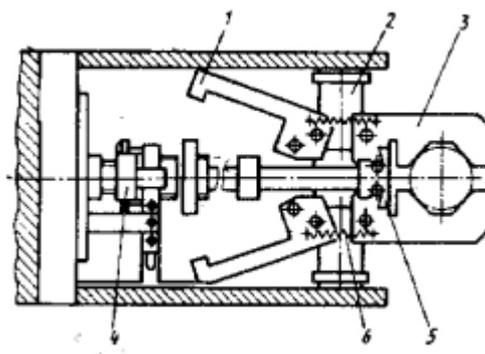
Захватное устройство с рычажными механизмами.
